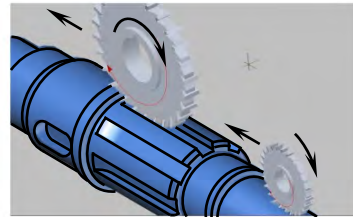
Выполнение технологических элементов вала согласно чертежу токарной обработки заготовки, полученной на 2-й стадии изготовления
